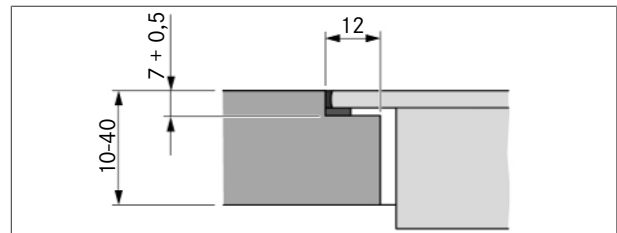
Dimensioni dell'incassatura per montaggio a filo piano
